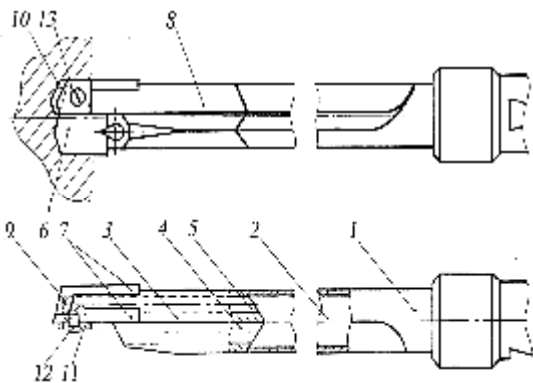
Ружейное сверло с высоконапорной подачей СОТС по передней и задней поверхности
